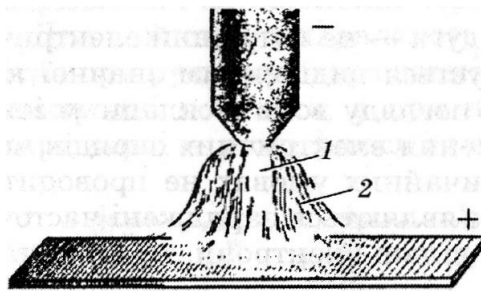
Зварювальна дуга, яка горить між електродом і металом:
